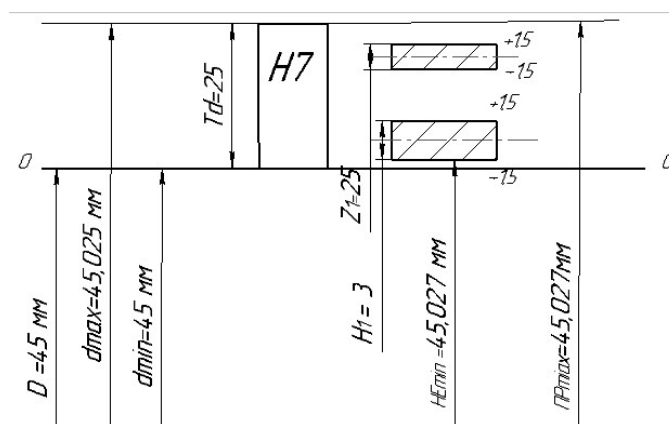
Схема розташування полів допусків для розміру $\varnothing 45H$
